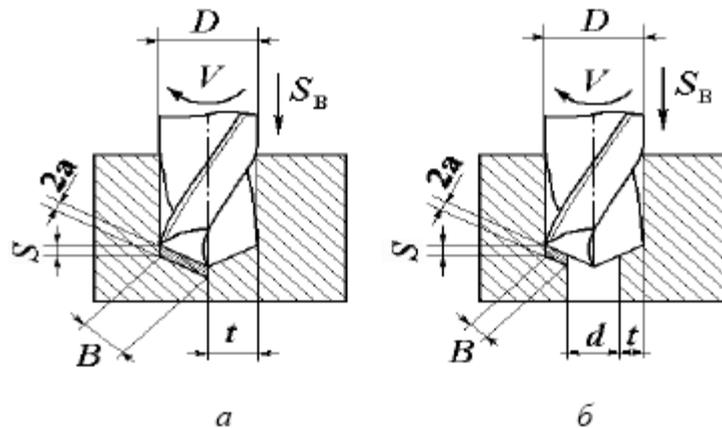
Схемы получения отверстий: а – сверлением; б– рассверливанием, где  $2a$  – толщина срезаемого слоя металла;  $B$ – ширина срезаемого слоя металла.
